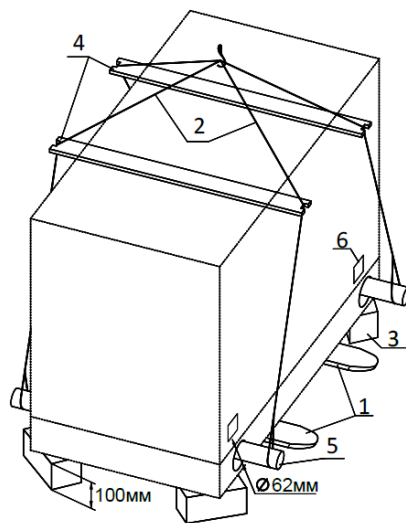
Схема строповки ККБ больших типоразмеров
